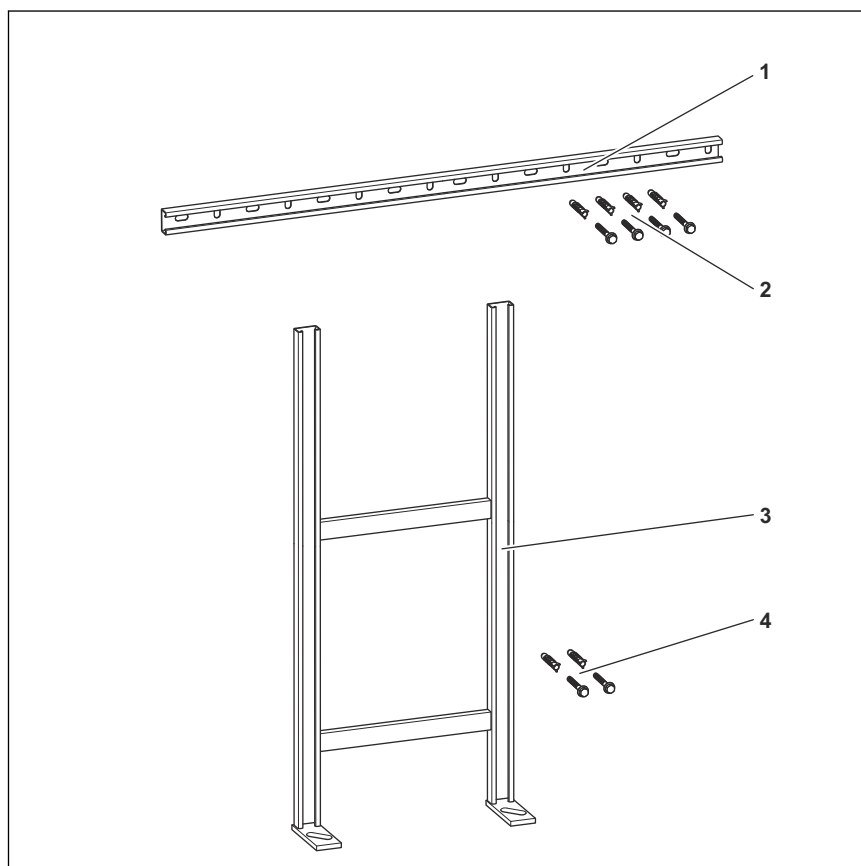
Acessórios para as variantes de montagem montagem em série e montagem em suporte
